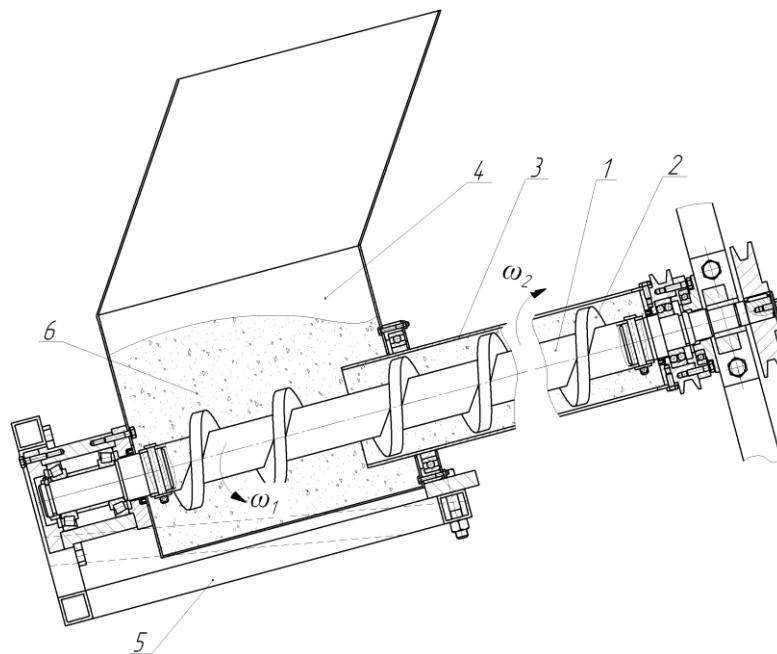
Конструкційна схема гвинтового конвеєра з обертовим кожухом: 1 – привідний вал; 2 – шнек; 3 – обертовий кожух; 4 – бункер; 5 – рама; 6 – матеріал, що переміщується
